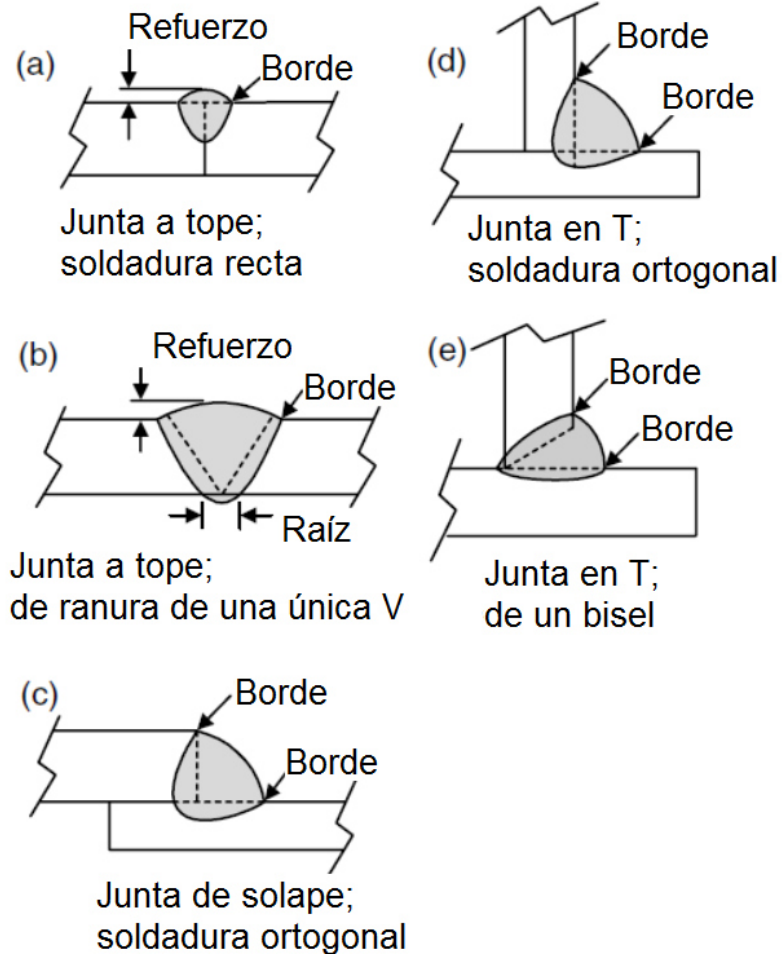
Variaciones típicas de las juntas de soldadura.
